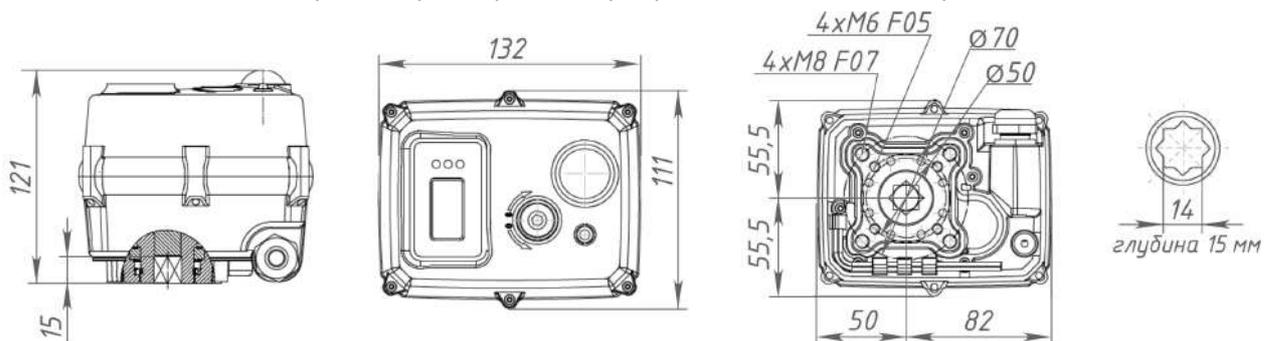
Габаритные размеры электроприводов Motorvalve серии Smart S50.
